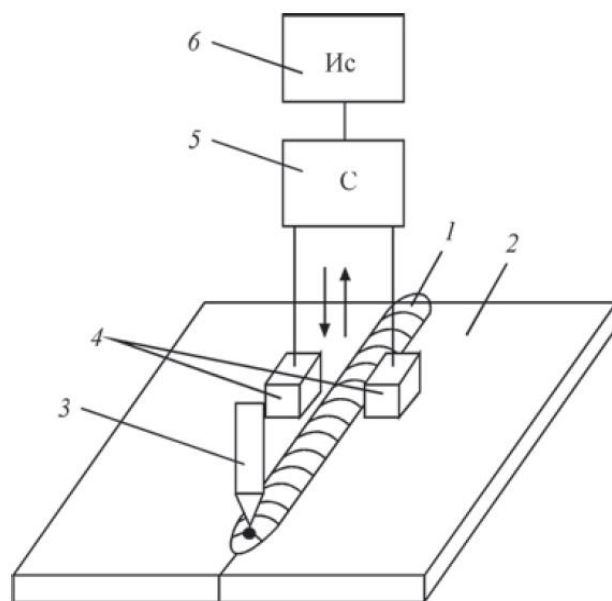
Схема установки для фоновой виброобработки: 1 — сварной шов; 2 — свариваемые детали; 3 — электрод; 4 — виброинструменты; 5 — синхронизатор; 6 — источник вибрации
